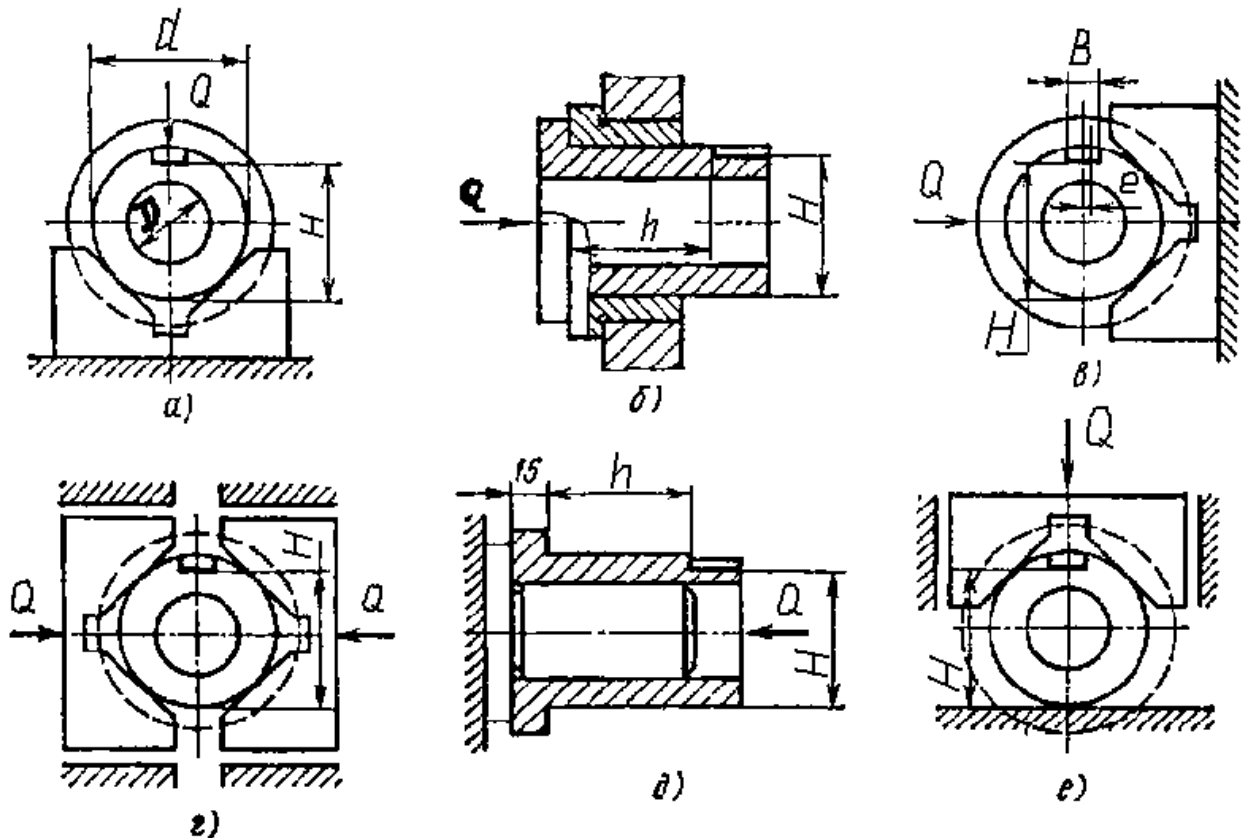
Схемы установки заготовки при обработке шпоночного паза (к задаче 14)
